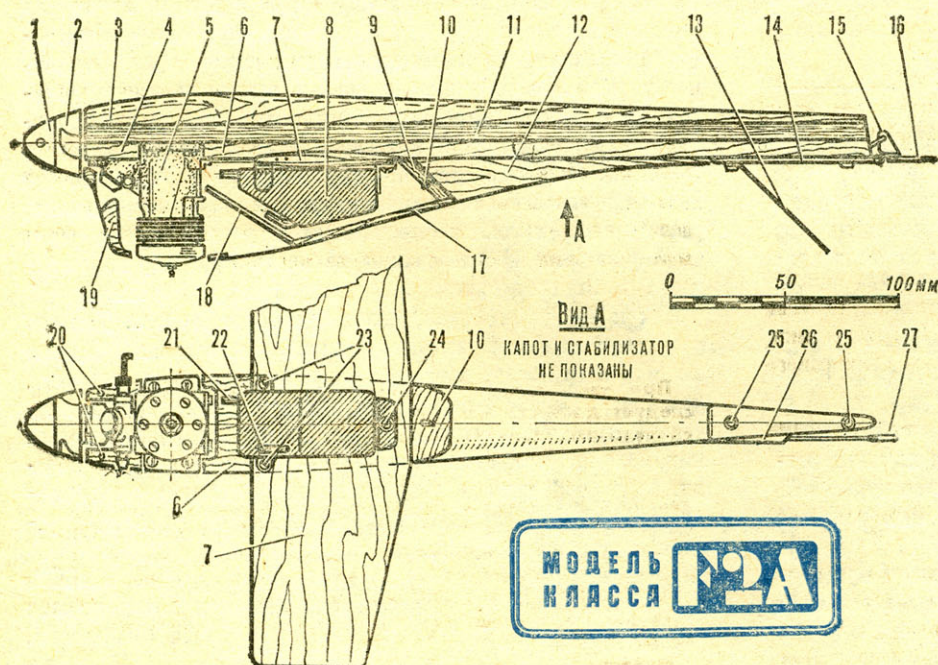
Конструкция фюзеляжа: 1 — кон-гайка (D16T), 2 — стаканчатый обтекатель воздушного винта (D16T), 3 — верхний обтекатель (липа, обогнуть), 4 — передняя накладка (липа толщиной 8 мм), 5 — двигатель ЦСТКАМ-2,5 К, 6 — основная накладка (липа толщиной 8 мм, обогнуть в зоне между крылом и стабилизатором, выдолбить канавку для тяги руля высоты), 7 — крыло, 8 — топливный бак (жест толщиной 0,3 мм), 9 — стенка обтекателя (липа), 10 — штырек фиксации задней части обтекателя (бамбук, клеить в хвостовом обтекателе), 11 — моторамы (фанера толщиной 8 мм, прорезать окно под картер двигателя, обогнуть за счет прорезки окон), 12 — хвостовой обтекатель (липа), 13 — костыль, 14 — стабилизатор, 15 — кабанчик, 16 — руль высоты, 17 — нижняя стенка обтекателя (фанера толщиной 1—1,5 мм), 18 — стенка-экран отвода охлаждающего воздуха и выхлопных газов (фанера толщиной 1 мм), 19 — обтекатель (липа), 20 — резьбовые гнезда под винты крепления обтекателя, 21 — трубка дренажа или наддува бака, 22 — трубка питания, 23 — винты крепления крыла и бака, 24 — задний винт крепления крыла и бака, 25 — резьбовые гнезда крепления стабилизатора, 26 — обтекатель выхода тяги, 27 — вильчатая оконцовка тяги руля.
